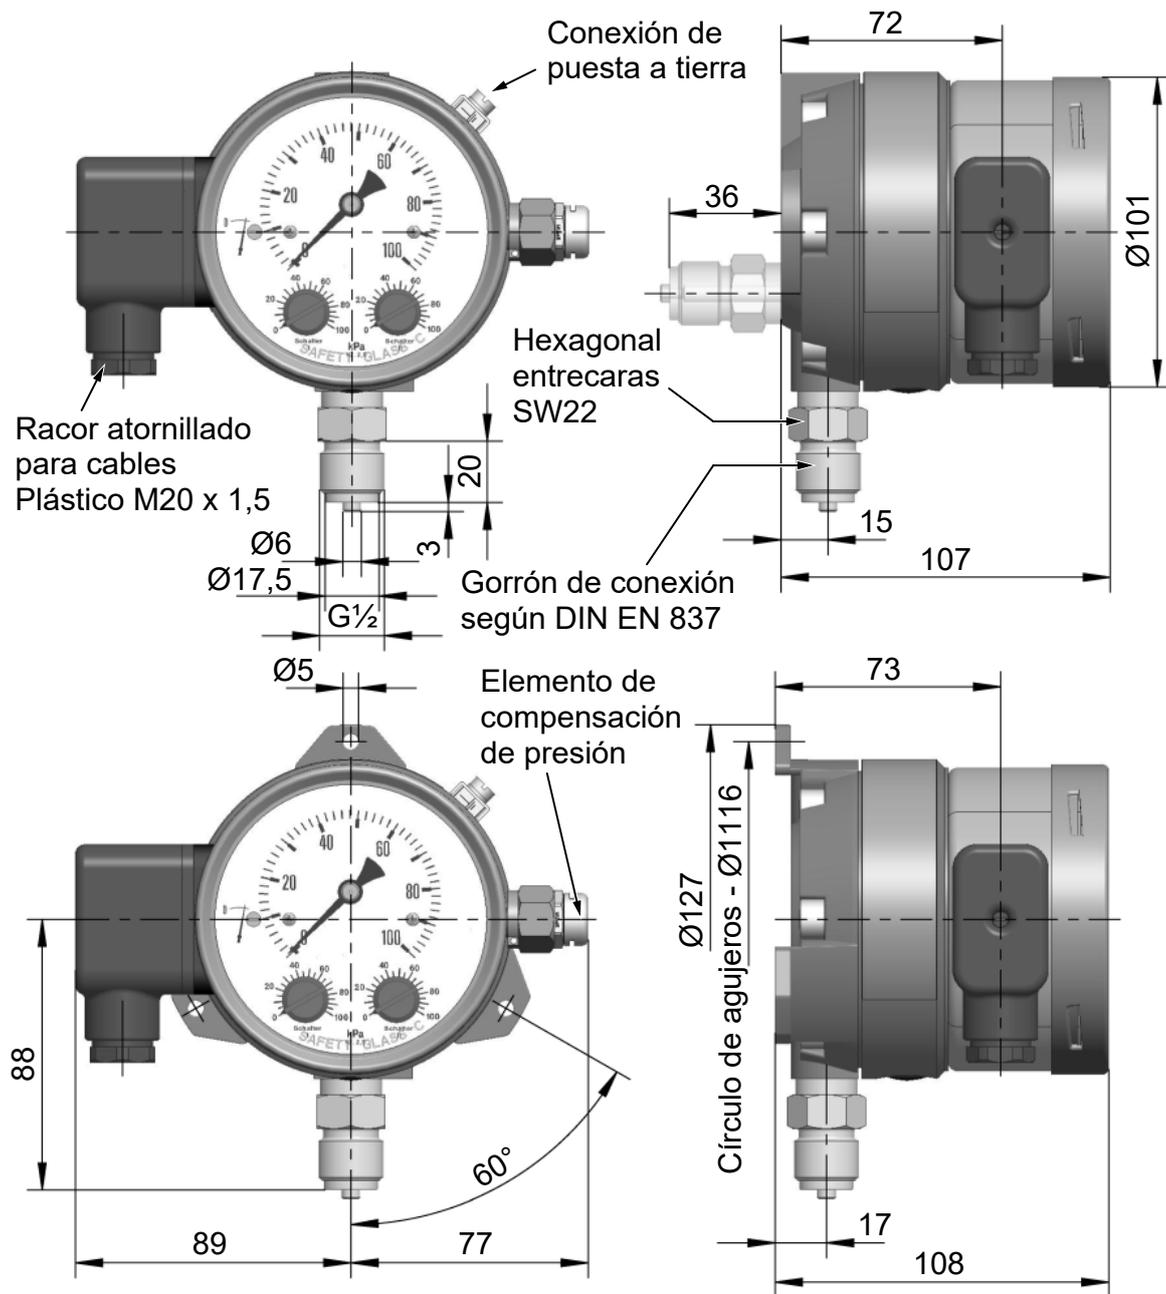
Cámara de presión de aluminio (ATEX) Montaje directo
